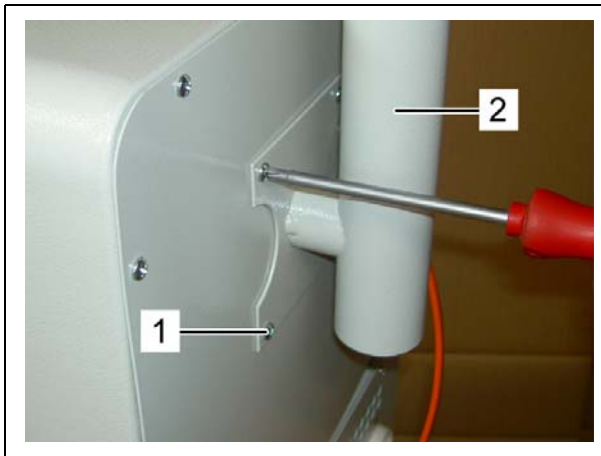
Schrauben (1) am Abzugsrohr entfernen
